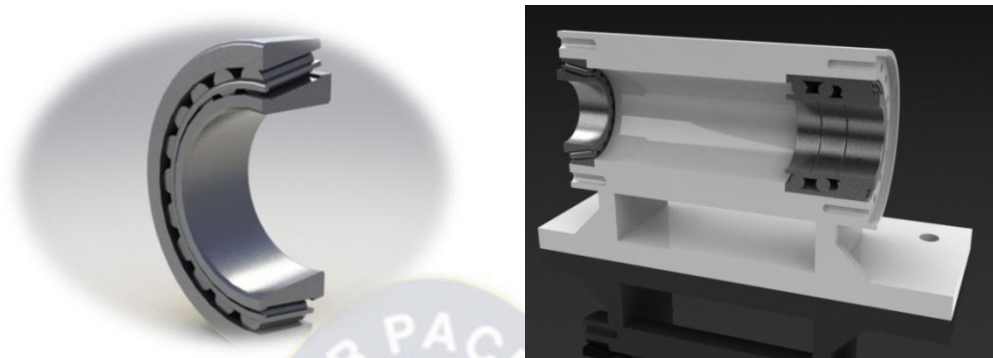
Rodamiento de rodillos cónicos y sección de la camisa con rodamientos.
